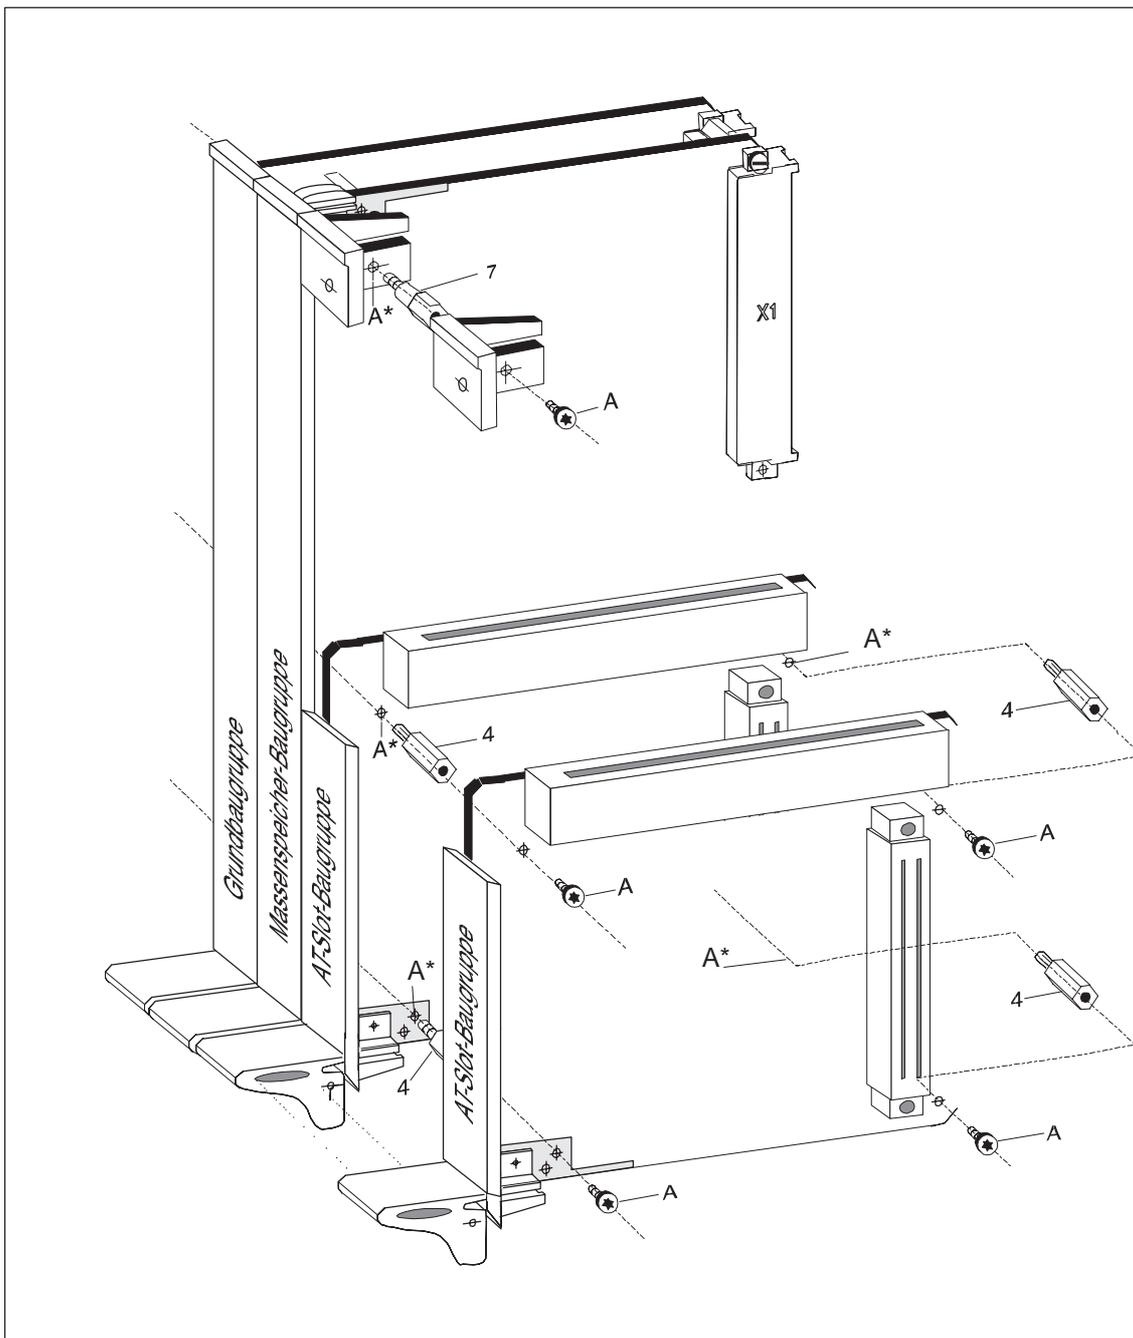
Montage von zwei AT-Slot-Baugruppen auf die Massenspeicher-Baugruppe
